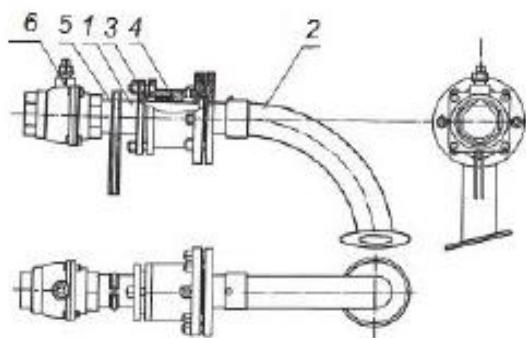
Кран сифонний: 1 - труба; 2 - відвід; 3 - втулка сальника; 4 - корпус; 5 - ручка; 6 - кран кульовий прохідний
